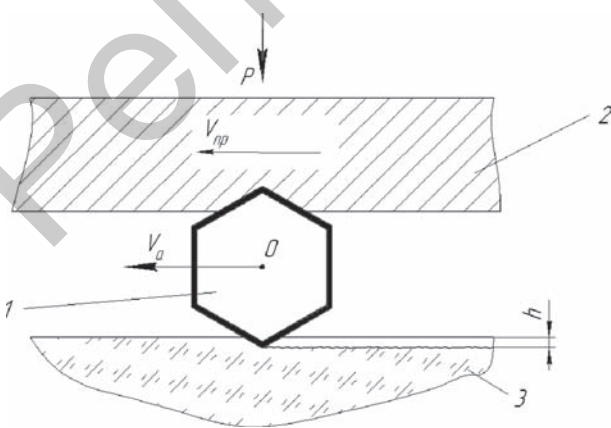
Схема контактного взаимодействия, закрепленного на поверхности инструмента абразивного (алмазного) зерна с обрабатываемой поверхностью заготовки
